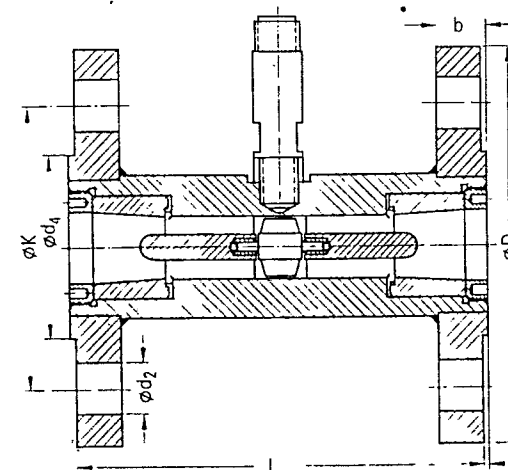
/5 Turbinen-Mengenmeßgerät mit Flanschanschluß, Maße
